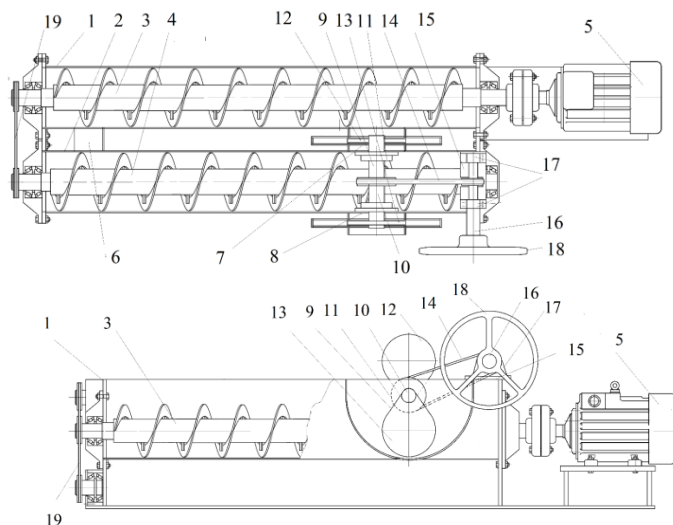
Принципиальная схема установки смесителя для производства арболита: 1,2 – корпуса; 3,4 – шнеки; 5 – электродвигатель; 6,7,8 – переходные камеры цилиндрической формы; 9 – отсекаль; 10 – вал; 11 – подшипниковый узел; 12,13 – диски цилиндрической формы; 14 – цепная передача; 15 – поворотное устройство; 16 – вал; 17 – подшипниковый узел; 18 – штурвал.
